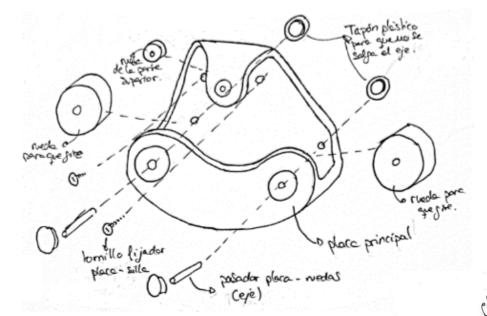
Explosión de la unión B de la rueda con tres ruedas pequeñas.
